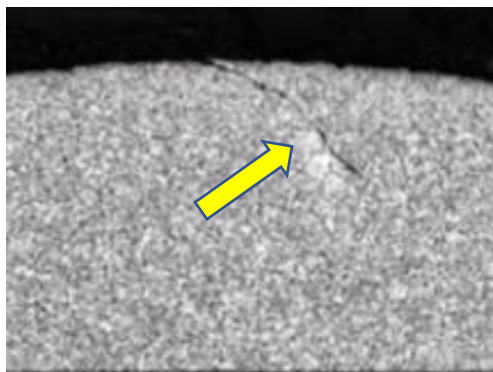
Corte de seção transversal de fio máquina com defeito de dobra. Fonte: LIMA, 2012.
